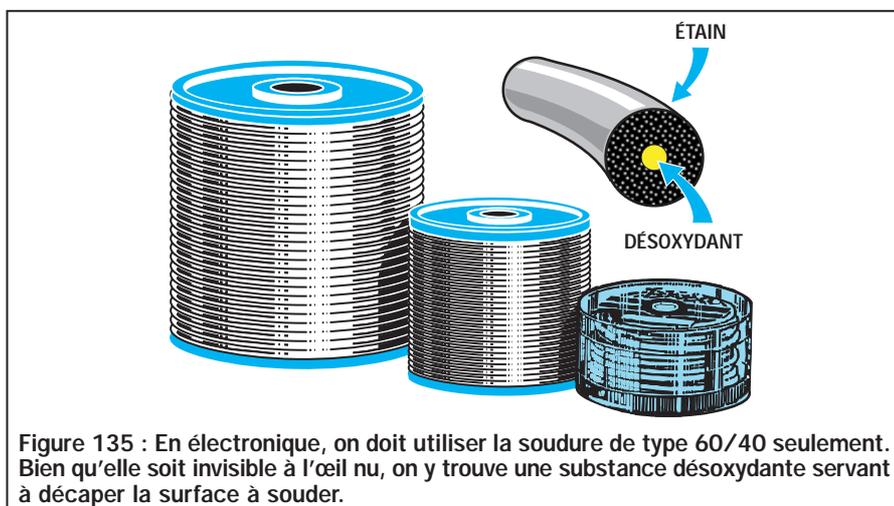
En électronique, on doit utiliser la soudure de type 60/40 seulement. Bien qu'elle soit invisible à l'œil nu, on y trouve une substance désoxydante servant à décapier la surface à souder.
